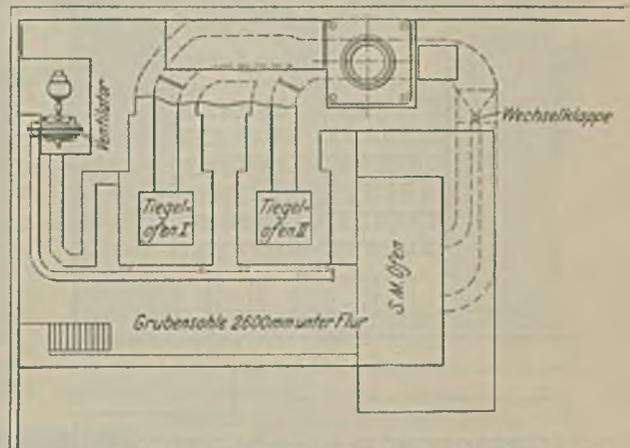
Grundriß der Öfen der Stahlwerksanlage.
